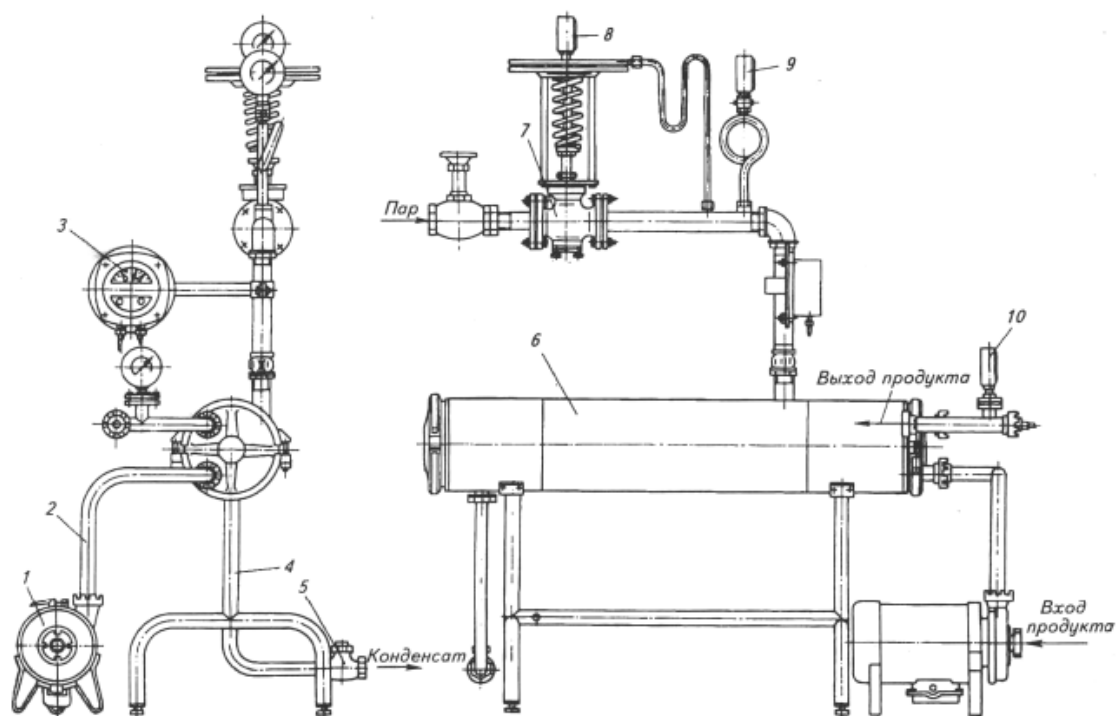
Трубчатый подогреватель П8-ОАБ:
